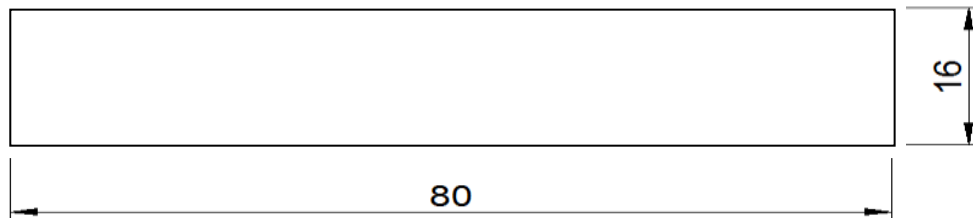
Esquema das dimensões dos provetes de flexão segundo a norma ASTM D 790 - 03 [85].
